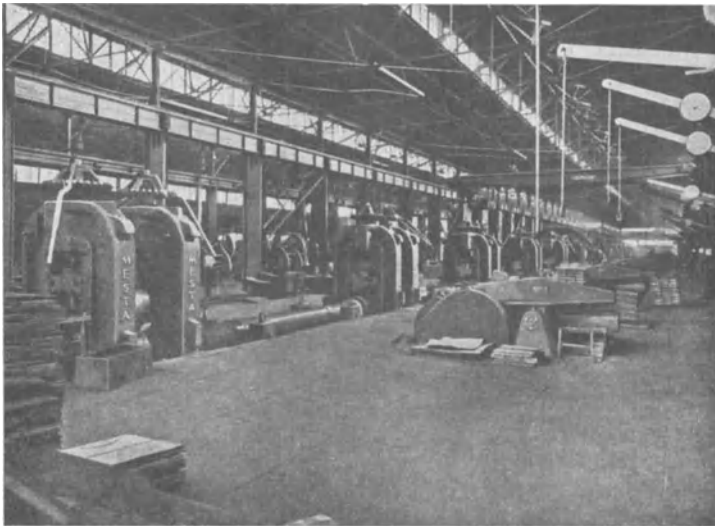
Feinblechwalzwerk der Trumbull Steel Co., Warren.
